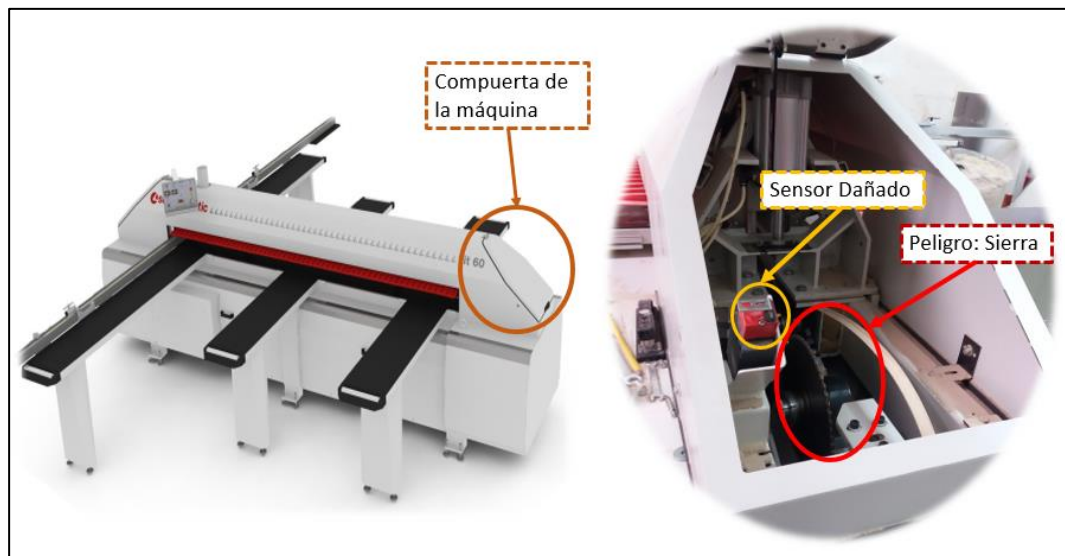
Ubicación del sensor dañado de la máquina cortadora de melamina
